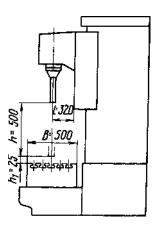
Габаритные размеры рабочего пространства станка модели 2Е78ПН
